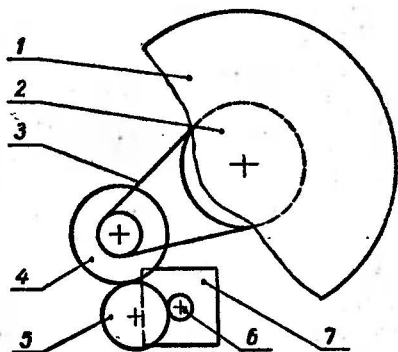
Кинематическая схема электропроигрывателя: 1 — диск проигрывателя; 2 — шкив-маховик; 3 — пассив; 4 — маховик промежуточный; 5 — обремененный ролик; 6 — насадка; 7 — электродвигатель
